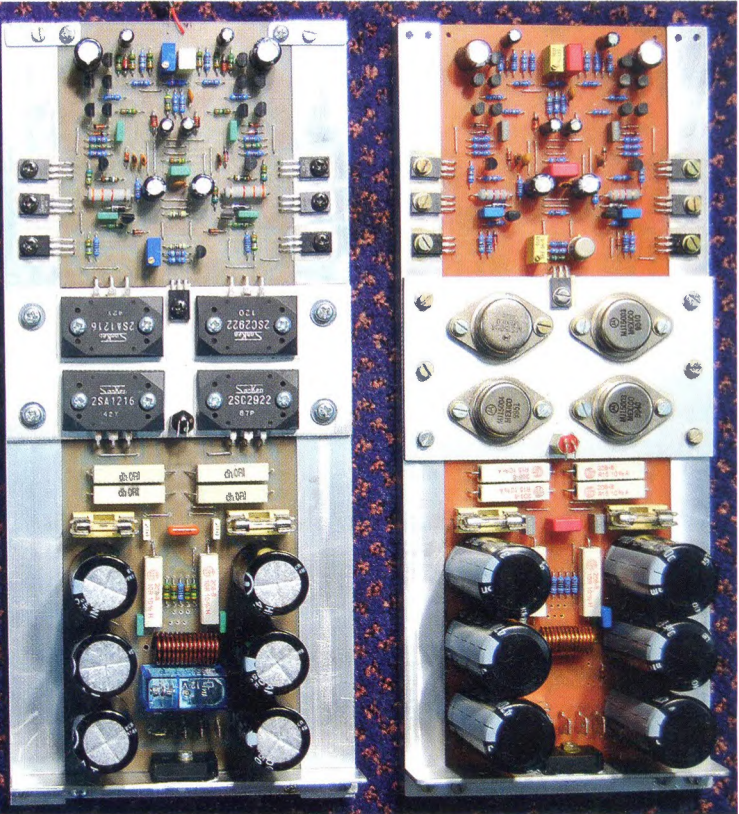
Deska s plošnými spoji modulu PSM 33 - horní strana
